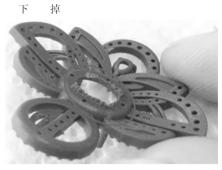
蜡模摆放角度与摆放位置的设定 Fig.3 Setting the angle and position of wax mold
